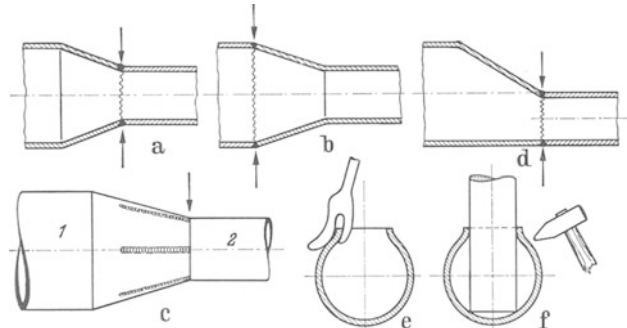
Schweißungen an Reduktionsstücken.
